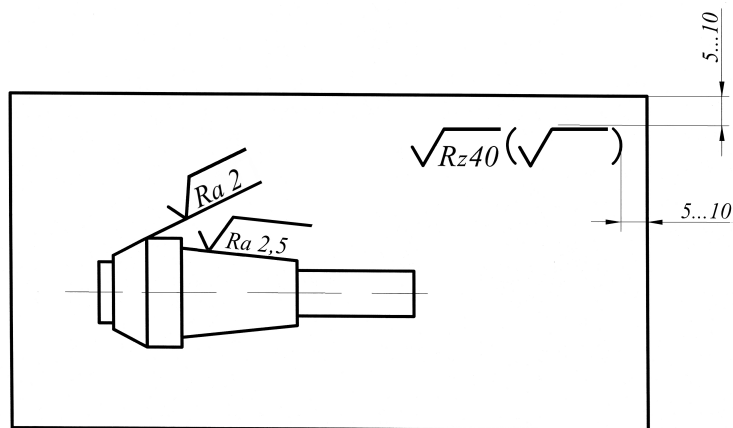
Обозначение шероховатости, когда все поверхности (кроме указанных) имеют одинаковую шероховатость
